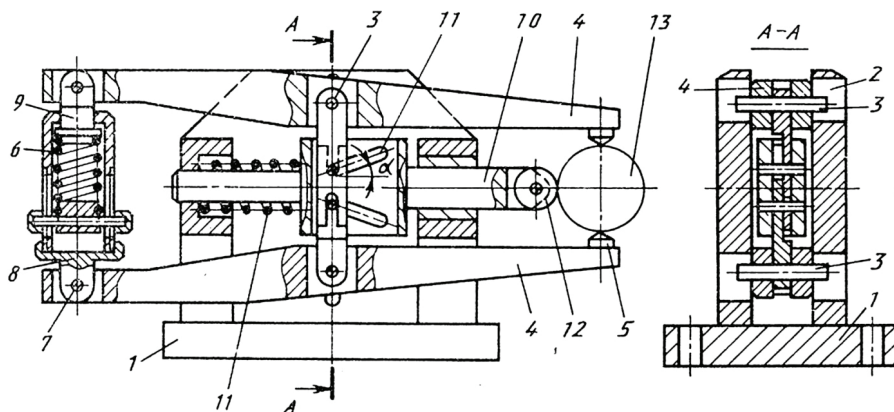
Двухалмазное копирное устройство: 1 – корпус; 2 – вертикальные окна; 3 – подвижные оси; 4 – несущие рычаги; 5 – деформирующие элементы; 6 – силовые пружины; 7 – ось; 8,9 – толкатели; 10 – шток; 11 – пружина; 12 – копирный ролик; 13 – обрабатываемая поверхность
